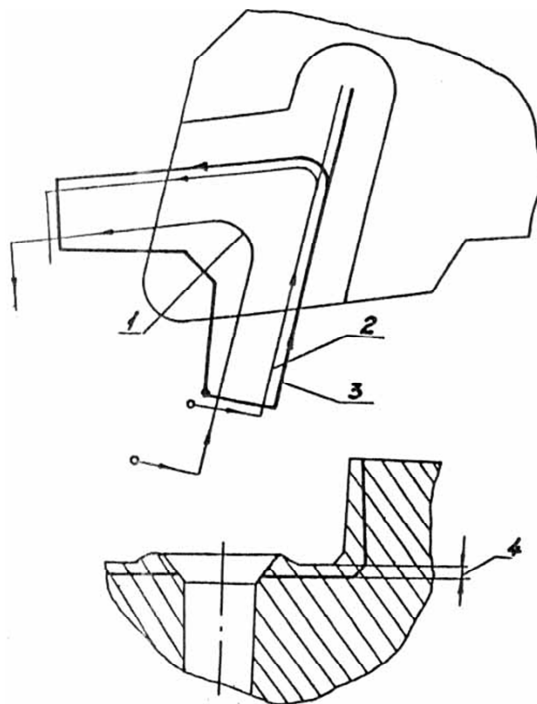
Особенности обработки дна гнезда под пластину в корпусах сборного режущего инструмента:
